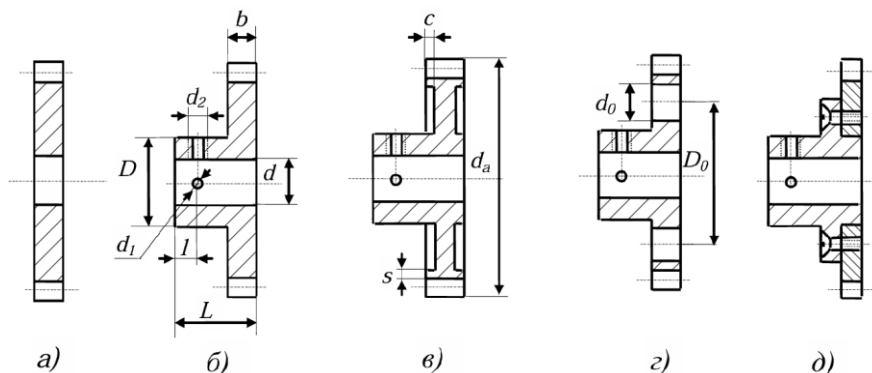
Конструктивные схемы выполнения зубчатых колес
